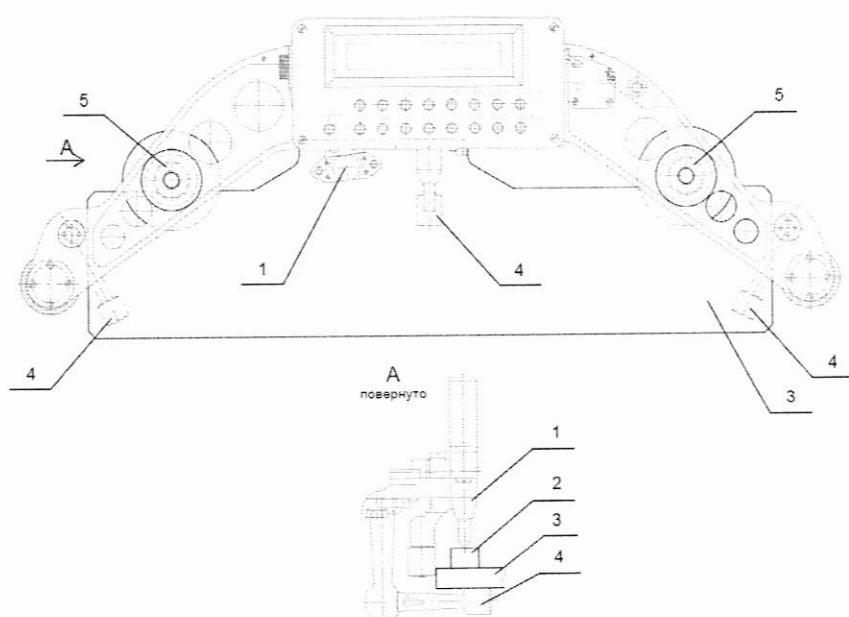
Установка приспособления для поверки ПП-МАИК.02.000 на прибор и порядок установки концевых мер длины
